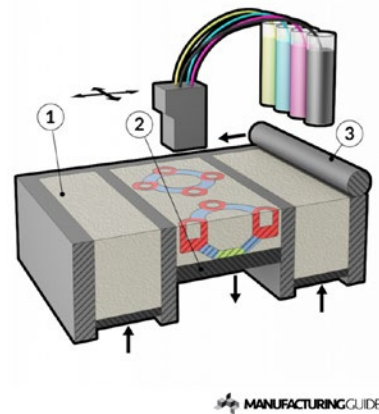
Schematische Darstellung des Binder Jetting Verfahrens, 1 Pulverlager, 2 Bauraum mit versenkbarem Boden, 3 Andruckrolle (www.manufacturingguide.com/en/binder-jetting 2023)
